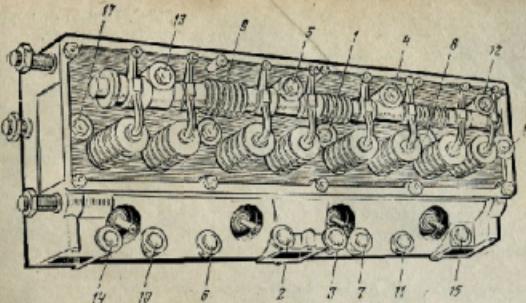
Порядок затяжения болтов крепления головки цилиндров
